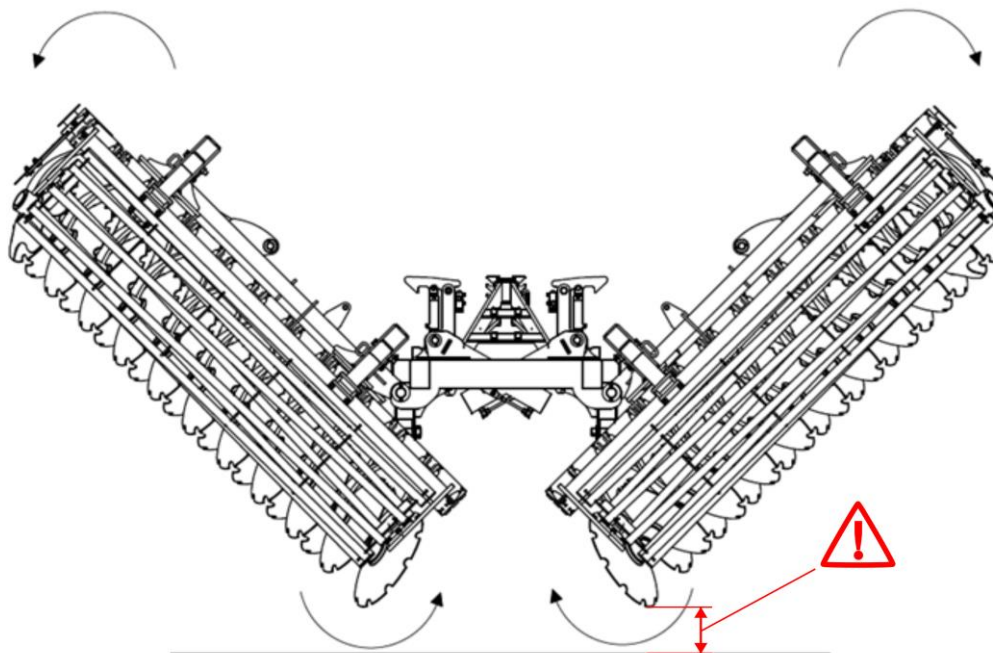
Séquence d'ouverture de la machine : ouverture de la machine en prêtant une attention particulière à la hauteur convenable des extrémités des bras par rapport au sol.
